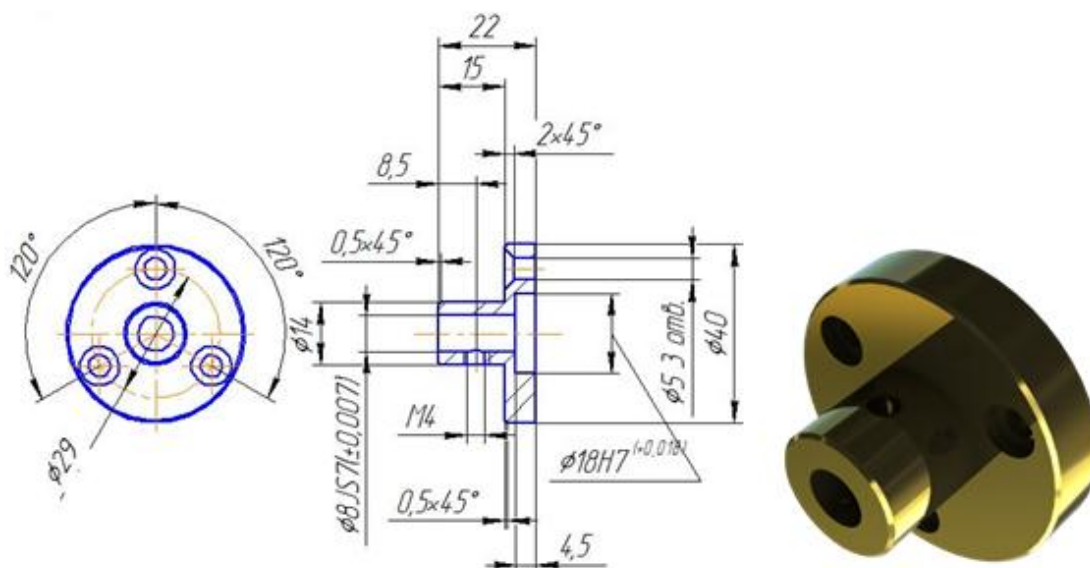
Чертёж и 3D-модель переходной втулки.
